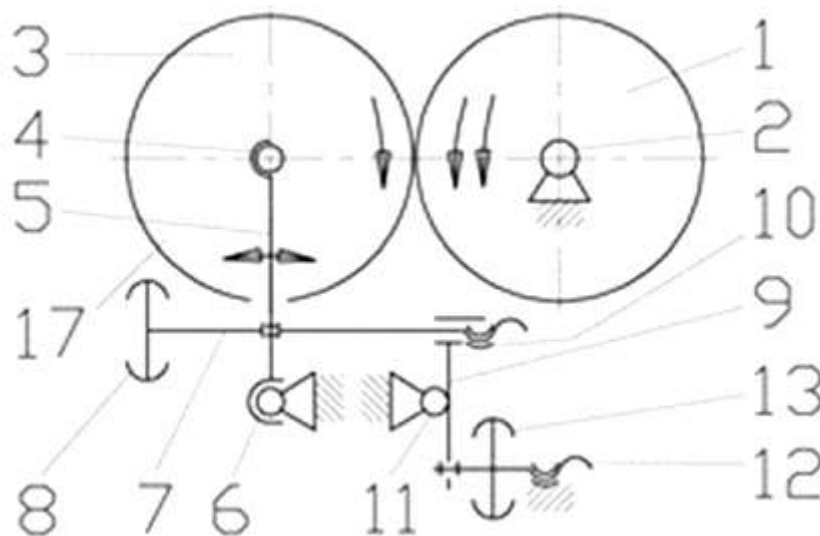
Схема установчого механізму вальцьового верстата.
